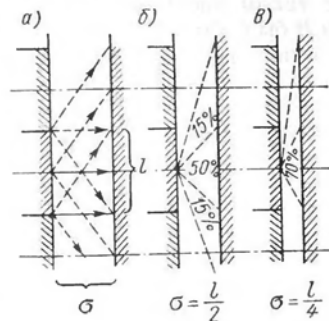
Схема распределения лучистой теплоотдачи боковой стенки укладочного приспособления
